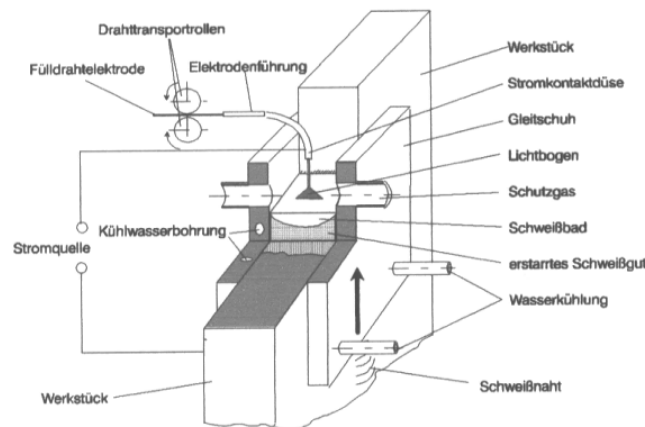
Verfahrensprinzip des Elektrogasschweißens
